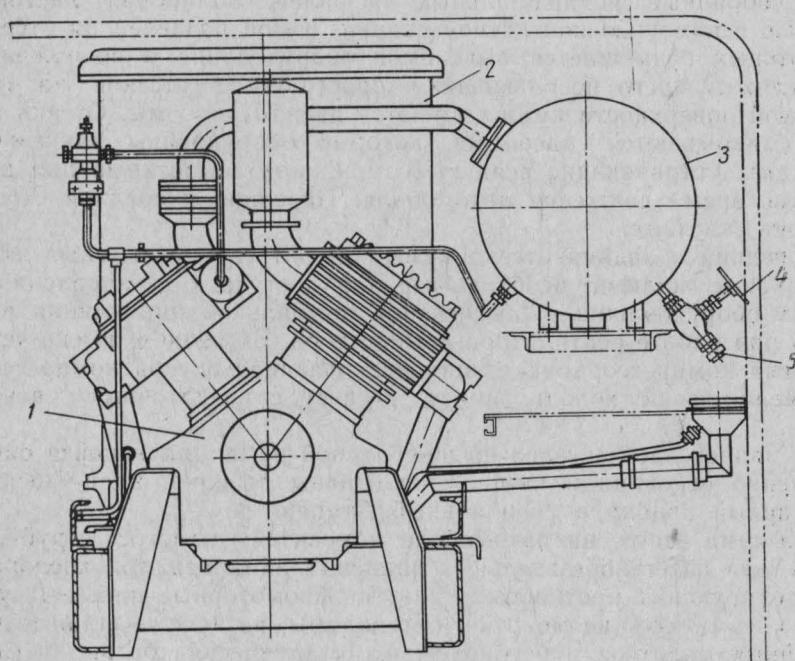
Компрессорная установка автомобиля АТ-2 (157К)
